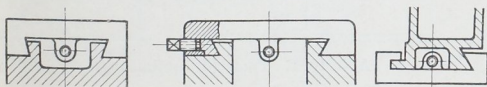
bis 1664. Schlittenführungen an Werkzeugmaschinen.
